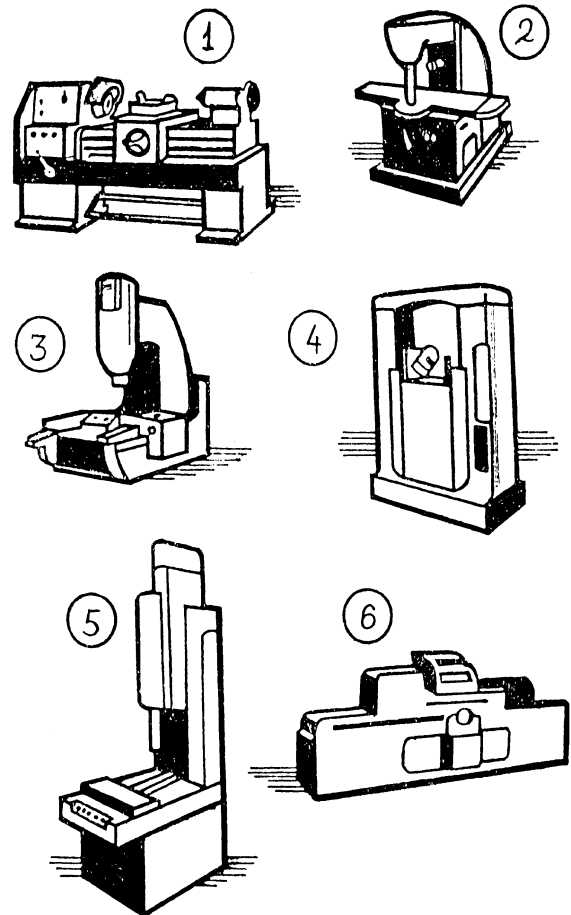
Proportionale Konstruktion von Werkzeugmaschinen /3/; 1-Drehmaschine, 2-Fräsmaschine, 3-Koordinatenausdrehmaschine, 4-Zahnfräsmaschine, 5-Hohnmaschine, 6-Schleifmaschine
